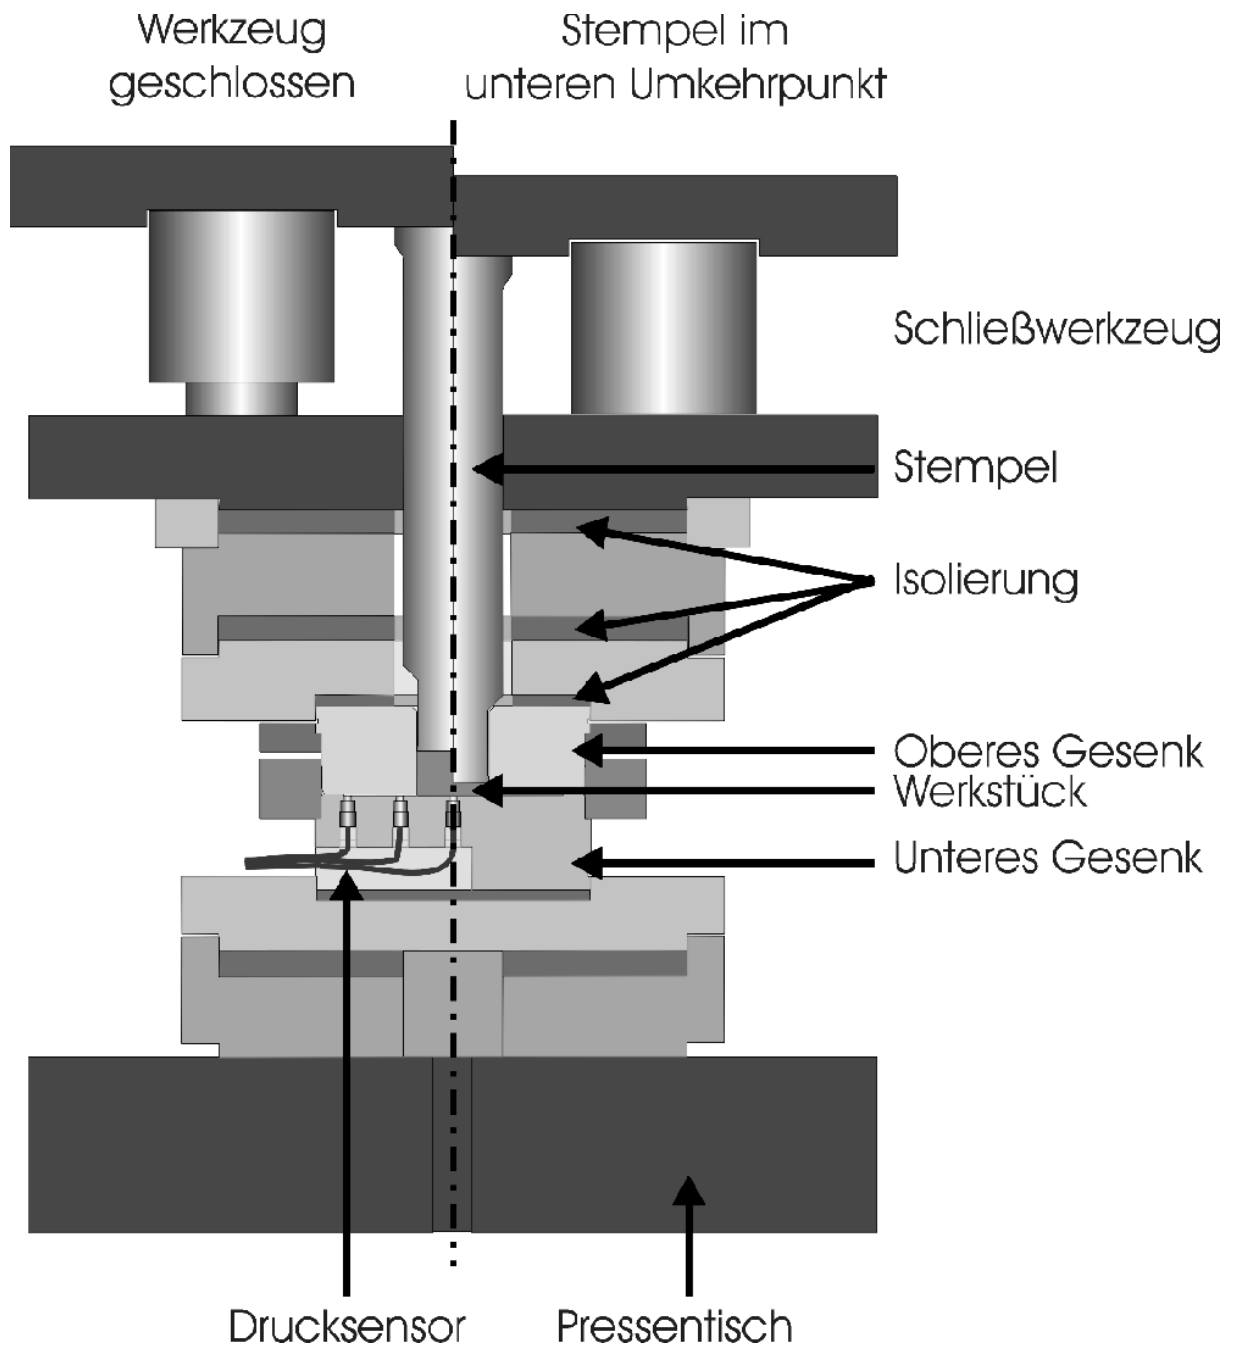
Schließwerkzeug mit Stickstoffedern und integrierter Druckmessung
